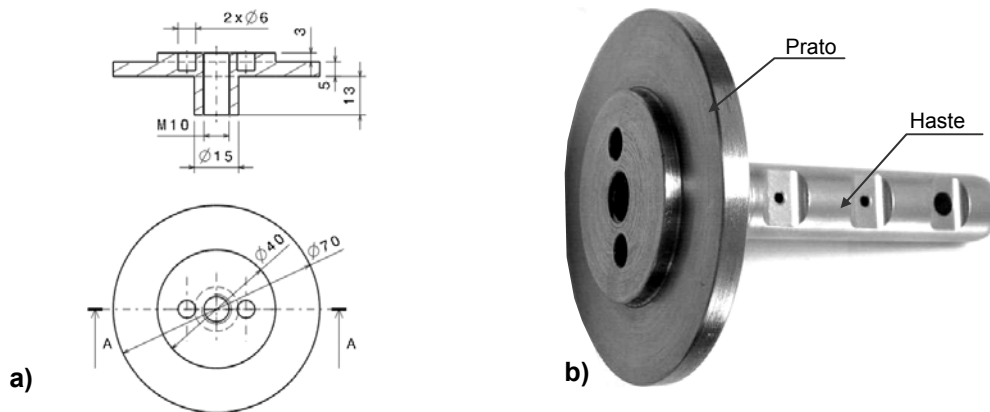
a) Dimensões nominais do prato; b) Conjunto prato-haste
